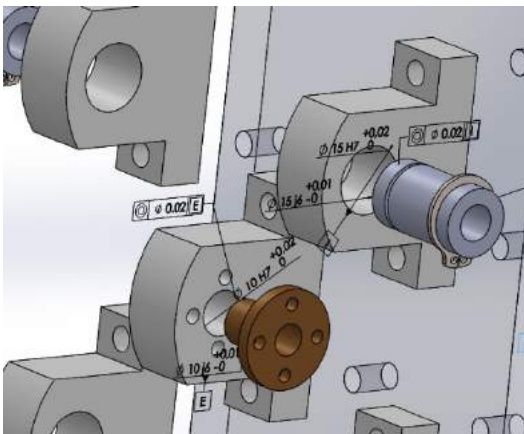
Tolerancias dimensionales y geométricas para rodamientos lineales
